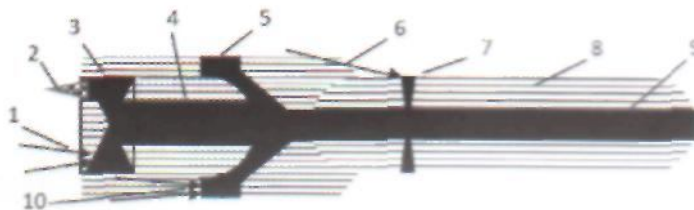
Багатокамерна детонаційна установка для нанесення покриття
